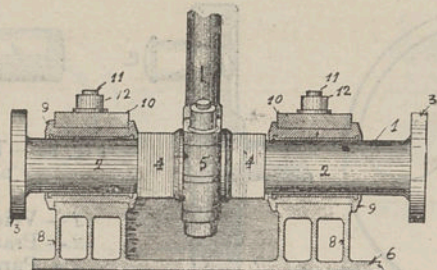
MANIVELLA, VEIO MOTOR E SUPORTES
